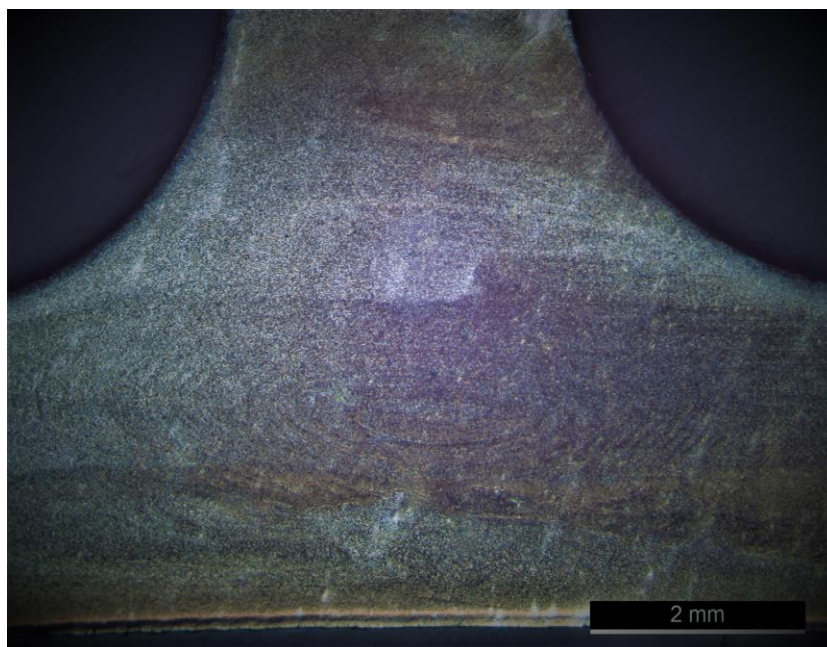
Macrografia da soldadura do coupon CRHP3, (ampliação 12.5x)
